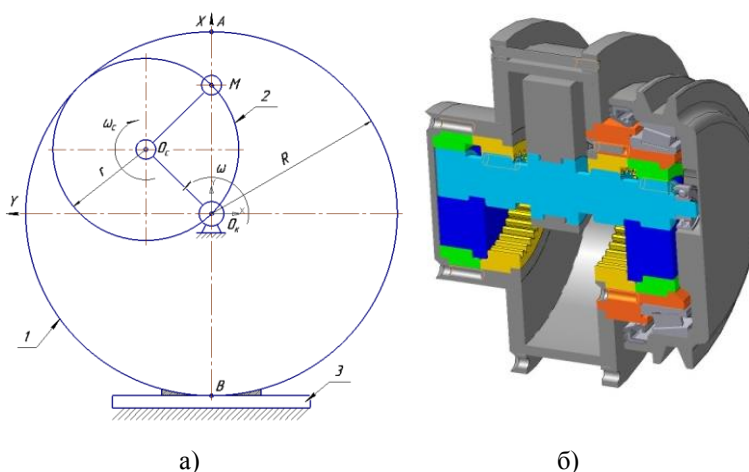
Схема планетарного механизма с соотношением диаметров колёс $D:d = R:r = 2:1$ (а), модель механизма (б). Здесь 1 - центральное колесо; 2 - сателлит; 3 - корпус; O_1 - центр колеса 1; O_2 - центр колеса 2; R, r - радиусы колёс 1, 2, соответственно; ω_1 - угловая скорость вращения радиуса O_1O_2 сателлита относительно центра колеса 1, т.е. т. O_2 ; ω_2 - угловая скорость вращения сателлита 2 относительно центра O_2 ; т. А, т. В - верхняя и нижняя точки вертикального диаметра колеса 1; М - точка сателлита, совпадающая с т.А в момент начала движения; обкатки сателлита по центральному колесу.
